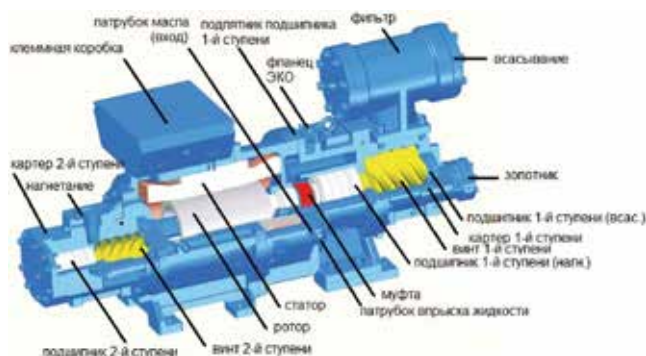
Винтовой двухступенчатый холодильный компрессор SRT
